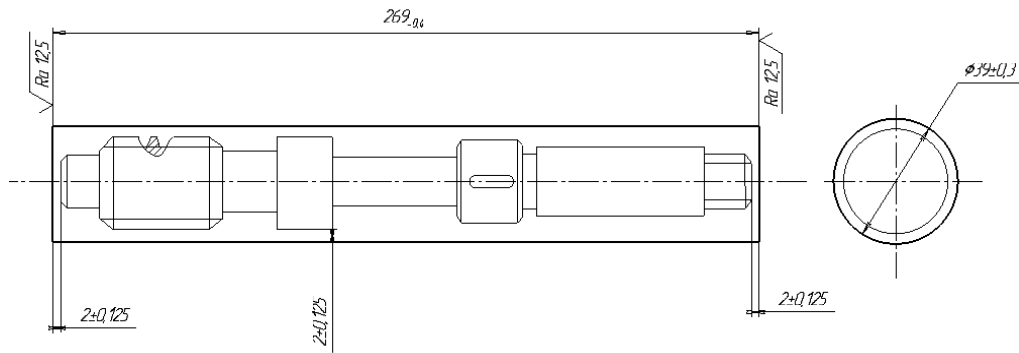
Ескіз заготовки із круглого прокату
